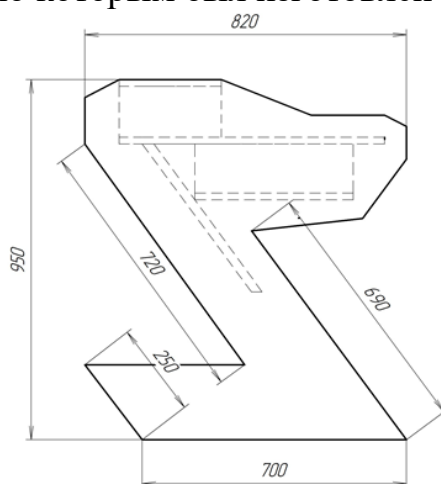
Чертеж боковой поверхности стола для звукоаппаратуры
